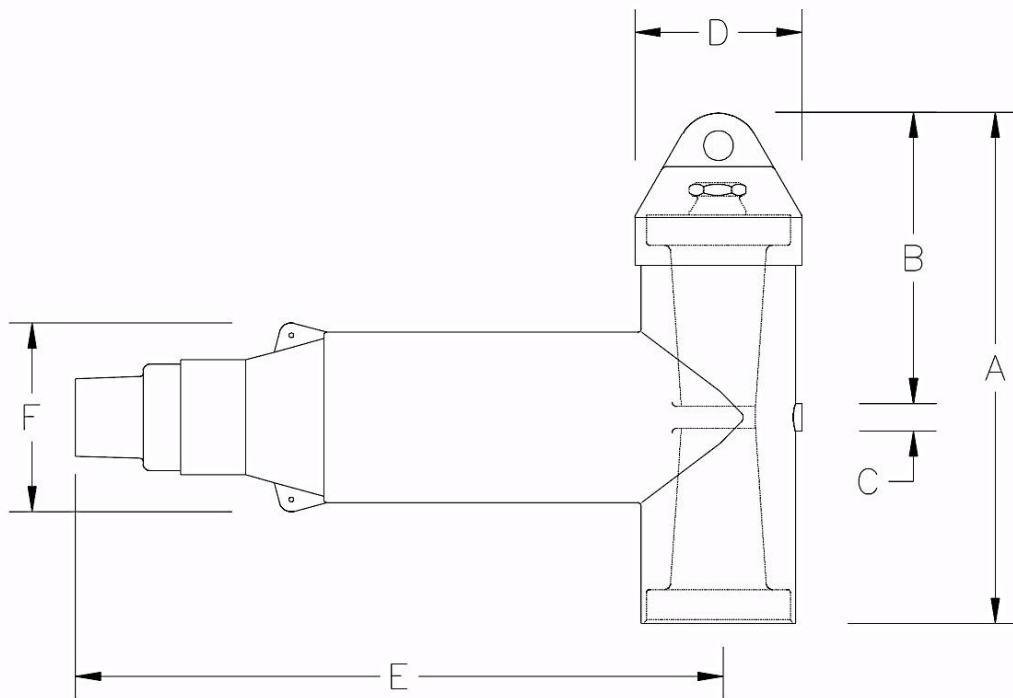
Dimensiones de terminal con cuerpo tipo “T”, [12].
